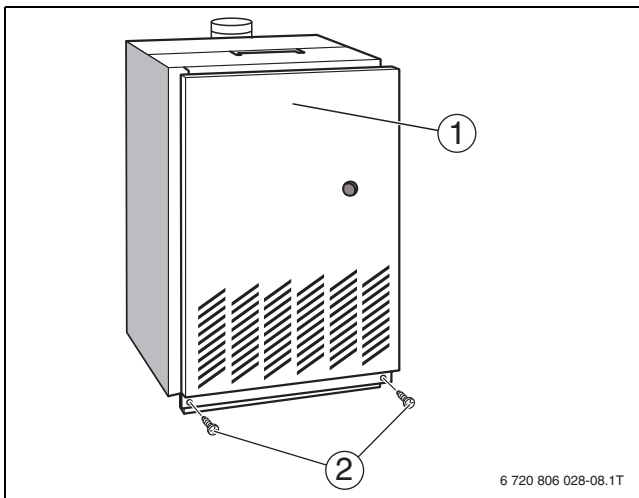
(Dé)montage de la paroi avant de la chaudière
